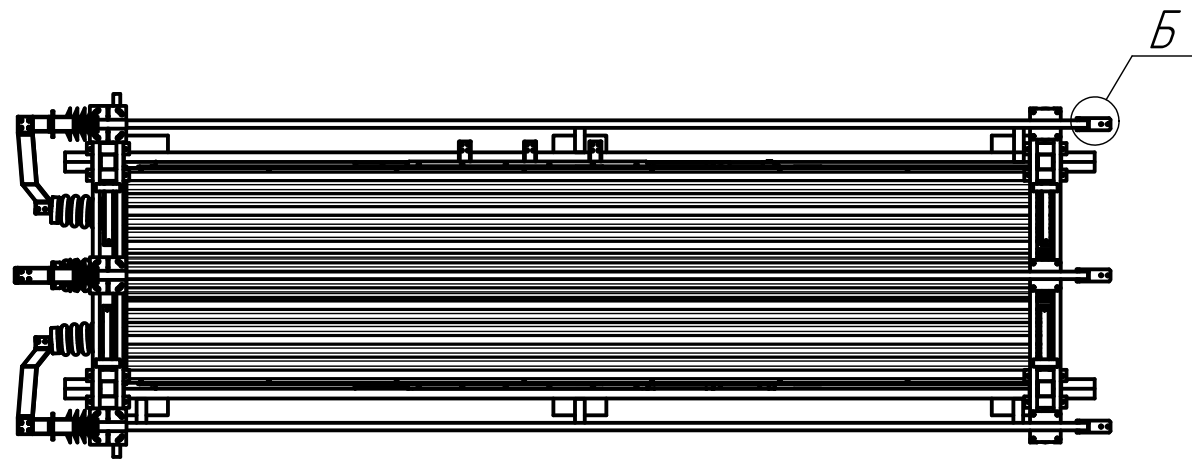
Проводка воздушной линии 1000А над зданием ЗРУ типа КРПЗ-35 У1
